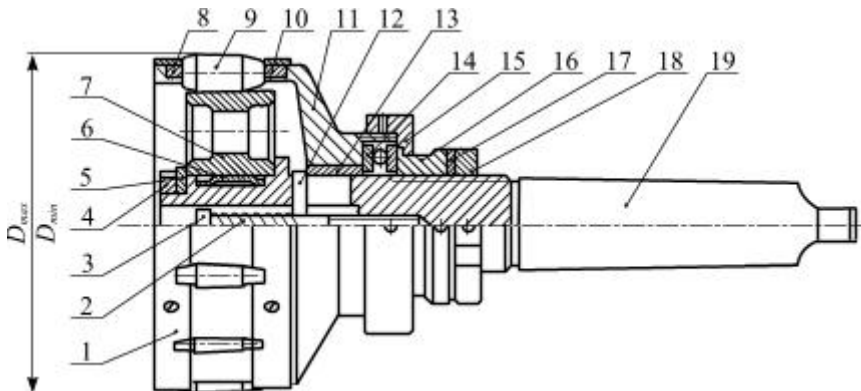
Розкатник багатороликовий: 1 – кільце; 2 – пружина; 3 – гвинт; 4, 15, 16, 18 – гайка; 5 – кільце; 6 – пружина; 7 – конус; 8, 10 – сухарі; 9 – ролик; 11 – сепаратор; 12 – ярмо; 13 – втулка; 14 – упорний підшипник; 17 – шайба; 19 – оправка
